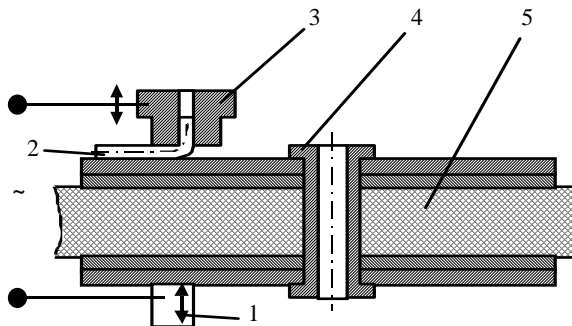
Схема сварки монтажных проводов:
